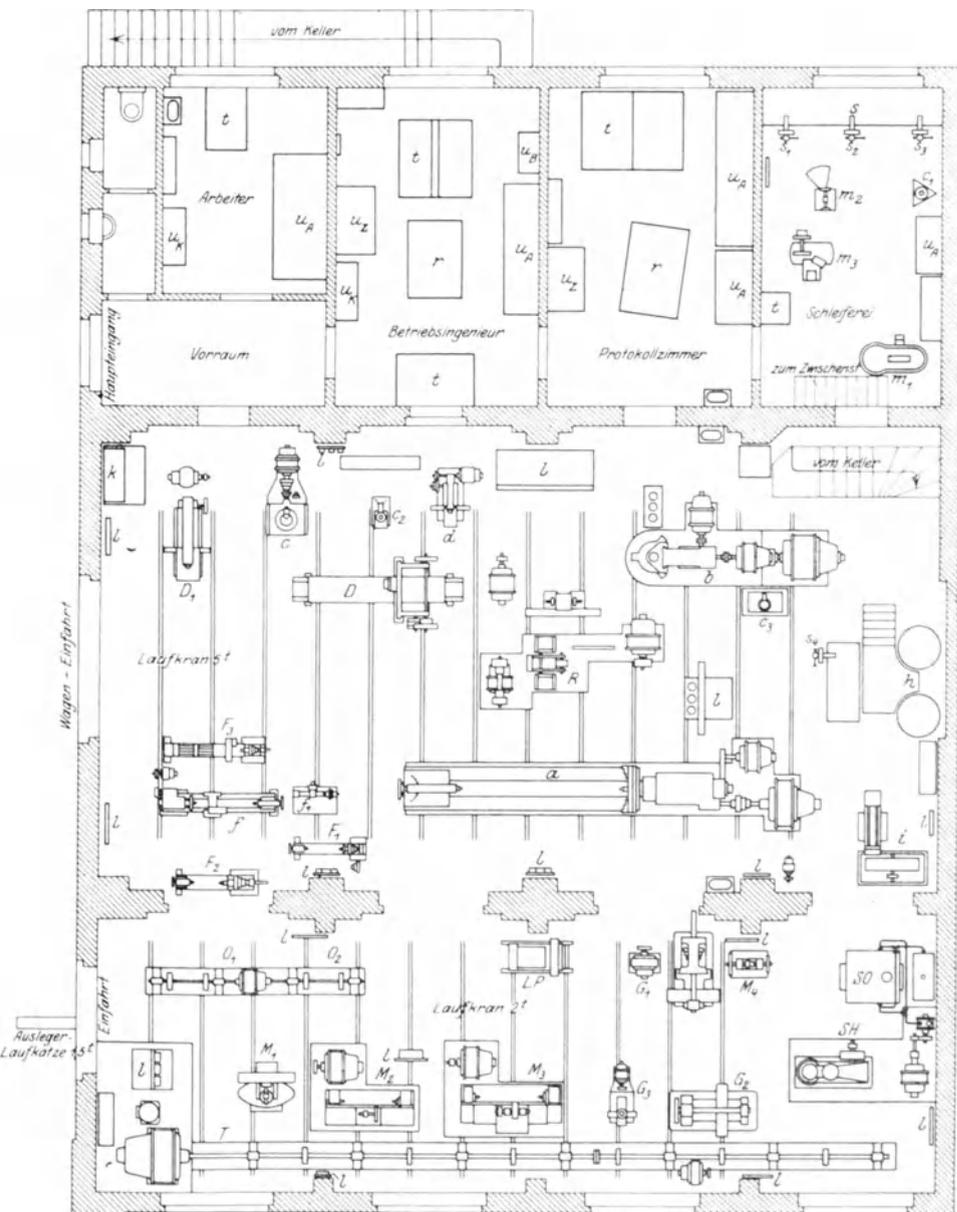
Grundriß des Versuchsfeldes für Werkzeugmaschinen (ebenerdig).
